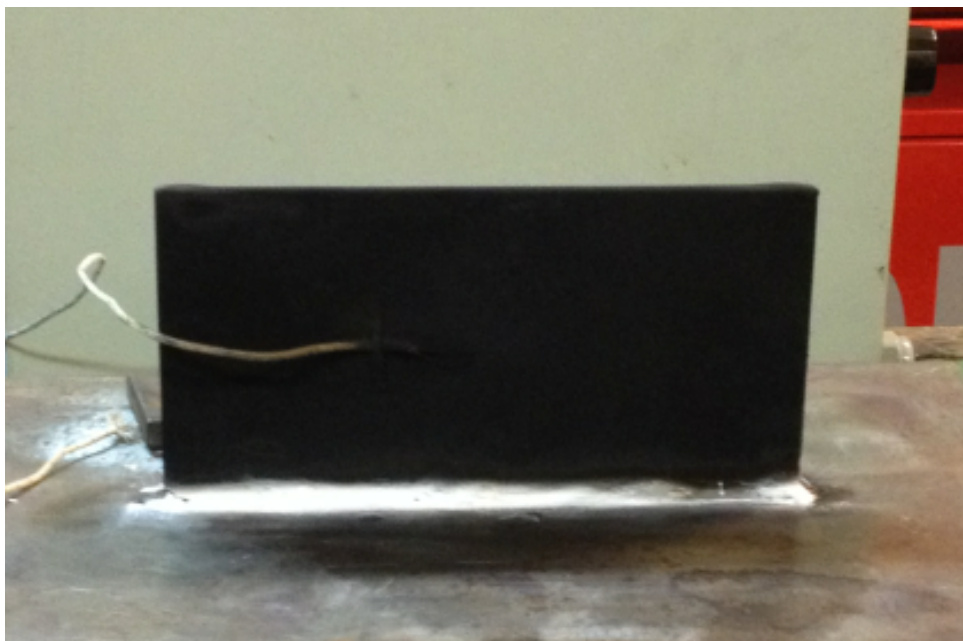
Placa de aço com fuligem sobre a superfície e pasta térmica nos espaços vazios, já soldada à mesa de trabalho e o termopar calibrado inserido ao centro.
